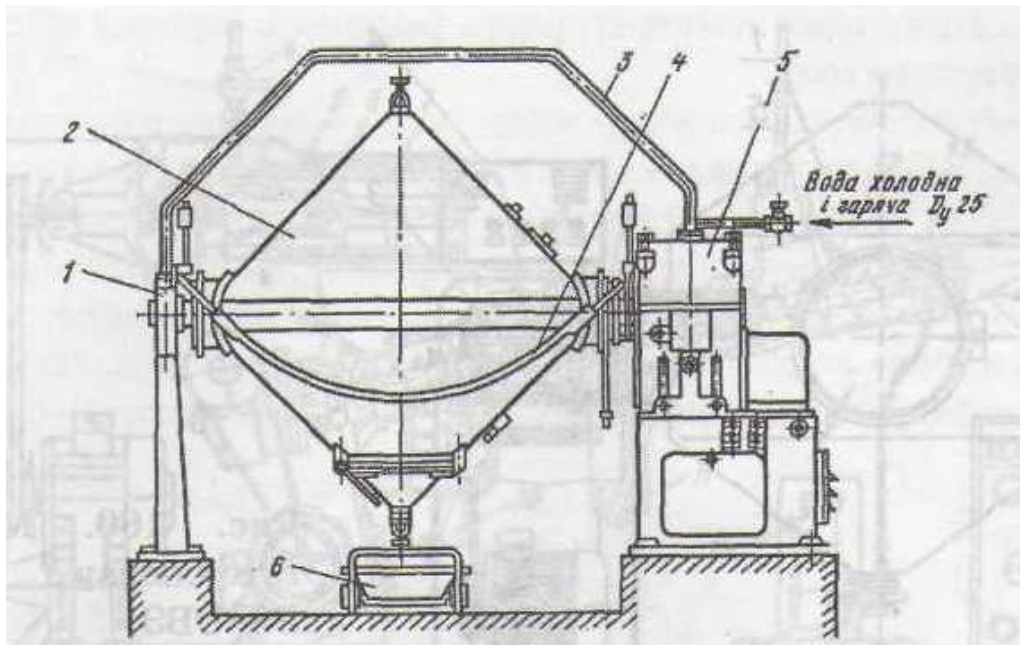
Безвальцьовий виготовлювач масла з конічною ємністю:
